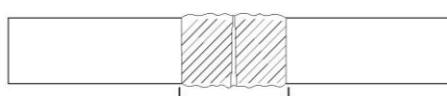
Test préalable pour un Temps de Soudure Adéquat - Illustration
